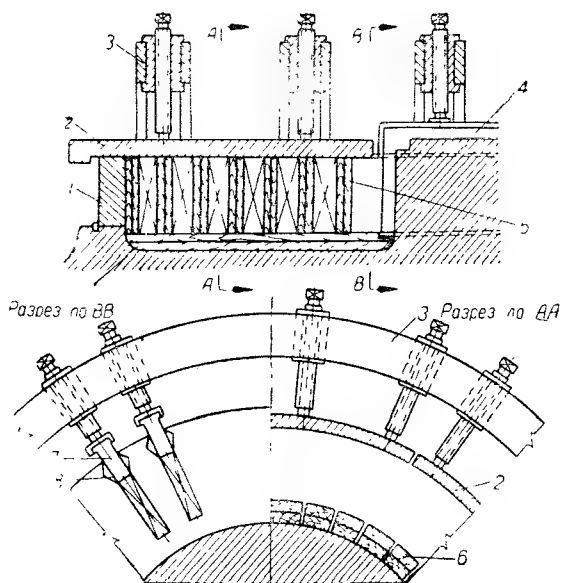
Прессующие приспособления для опрессовки роторных обмоток:
